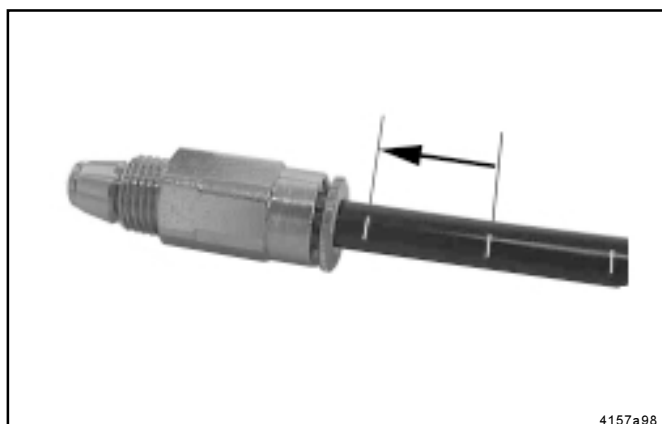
Rückschlagventil mit gerändelter Zange und Druckkunststoffrohr
